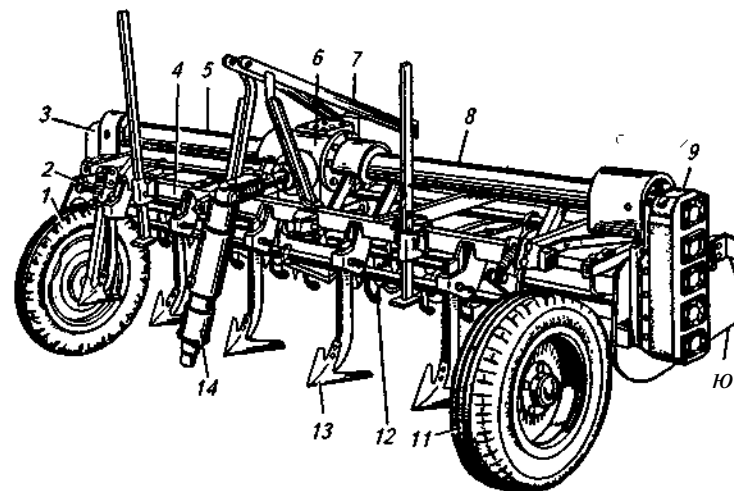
Культиватор-глубокорыхлитель КФГ-3,6:
